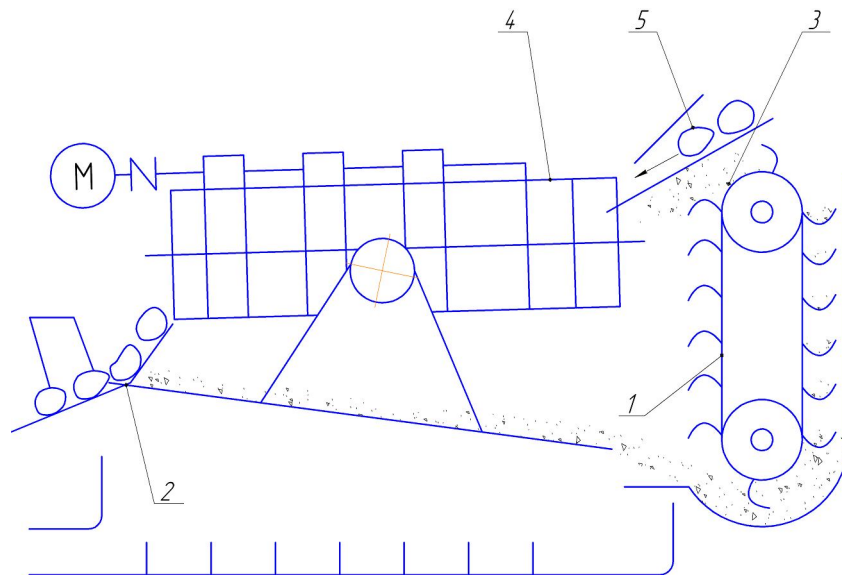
Принципова схема вібраційної машини безперервної дії з трубчатим секційним контейнером: 1 – стрічковий конвеєр; 2 – розділювальний пристрій; 3 – робочий наповнювач; 4 – контейнер; 5 – продукція, що обробляється
